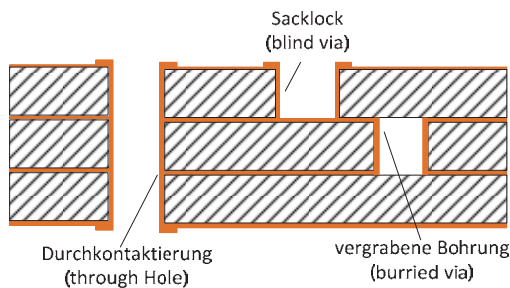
Durchkontaktierungen in verschiedenen Ausführungen
